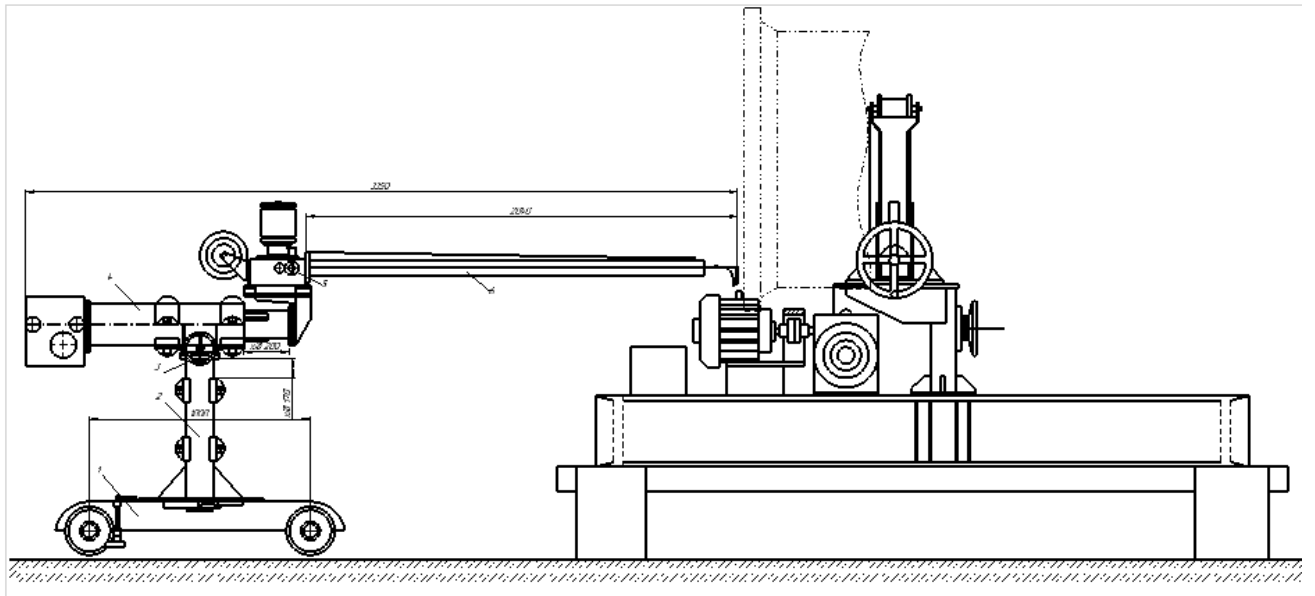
Установа для зварювання внутрішніх швів
